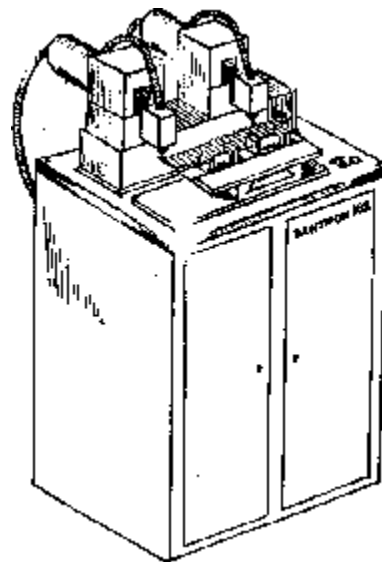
Внешний вид установки ЭЛИТРОН—182
